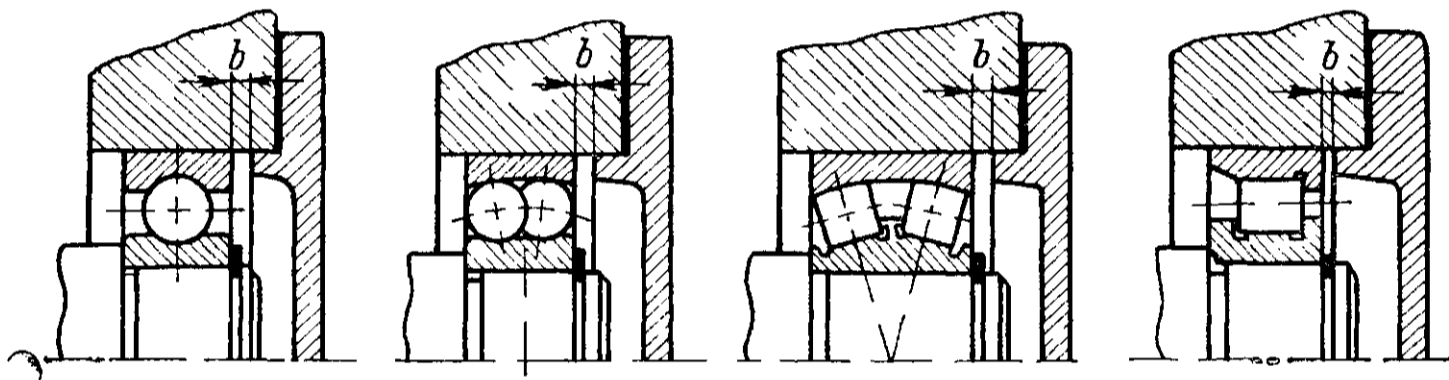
Некоторые конструктивные варианты шарнирно-подвижных опор валов с подшипниками качения
